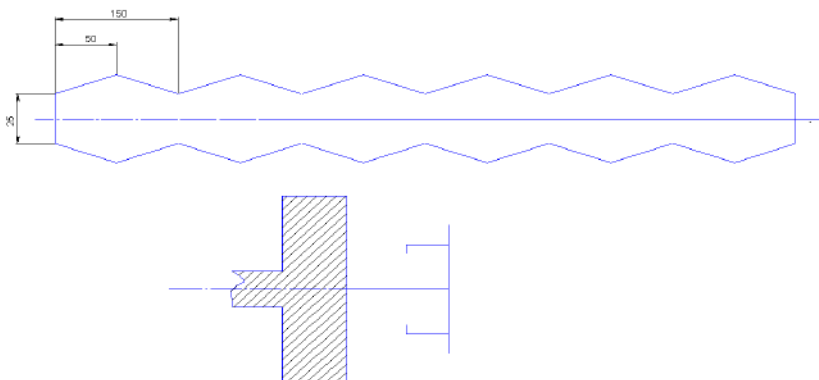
Чертёж и условные размеры зубчатого спойлера
